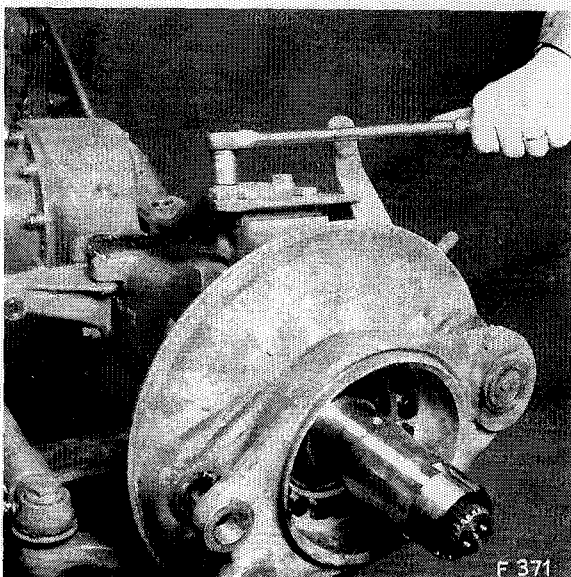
Lösen der Befestigungsschrauben für den Lenkhebel
